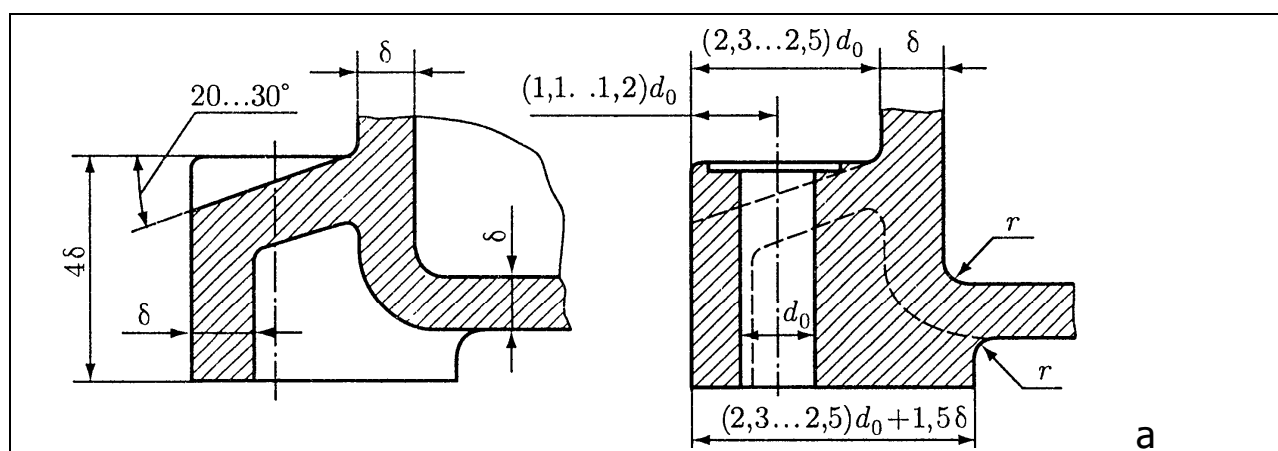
Резьбовые соединения корпуса и крышки редуктора по плоскости разъема. Размеры конструктивных элементов:
